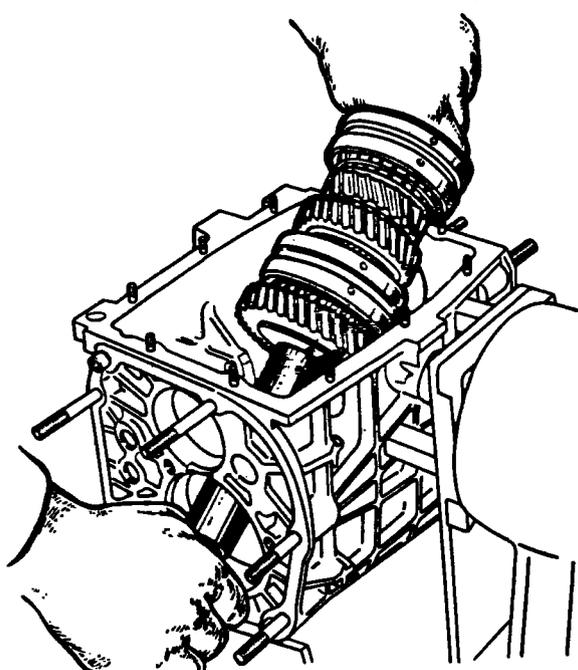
Извлечение вторичного вала из картера коробки передач
